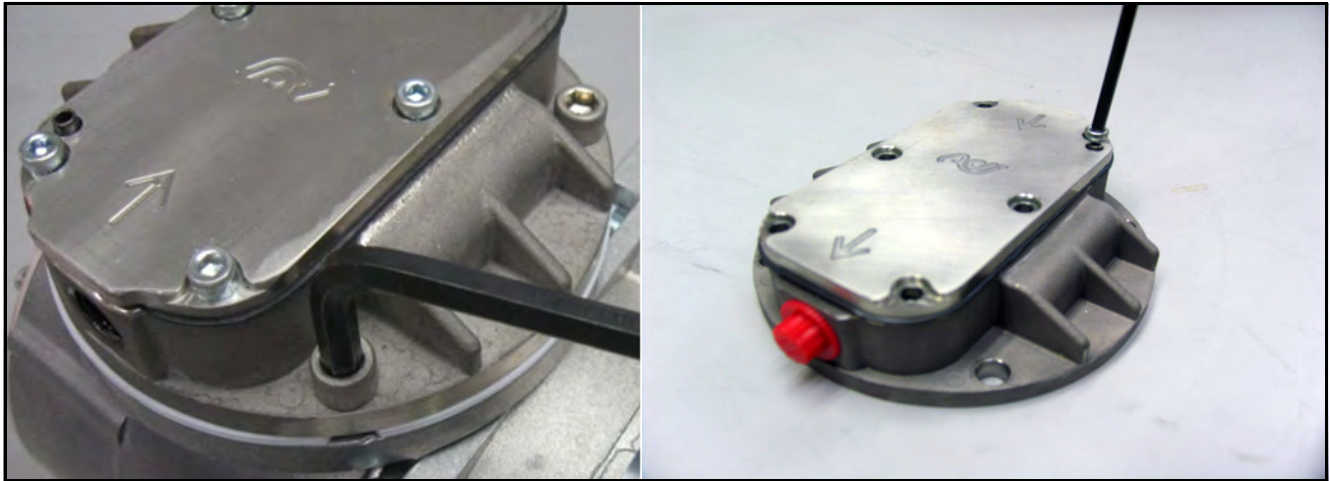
Entfernen des Kopfstücks und der Inbusschrauben
